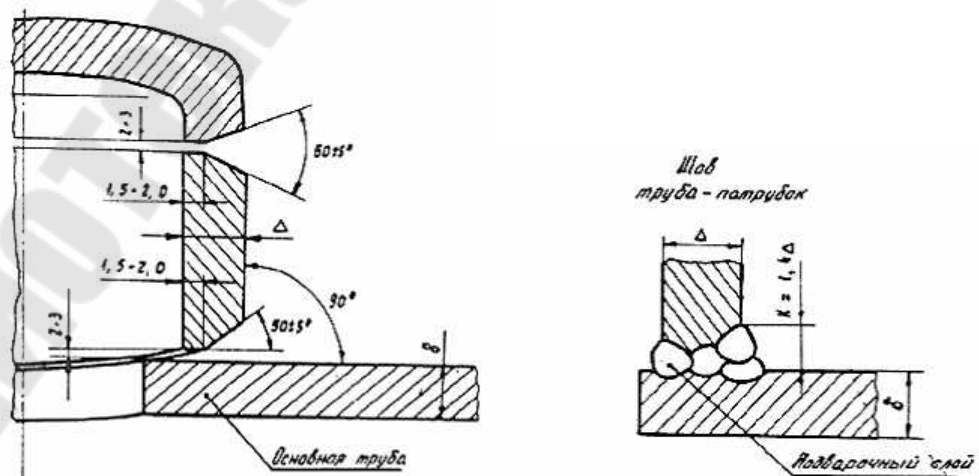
Схема подготовки под сварку при заделке технологических отверстий с помощью патрубков
